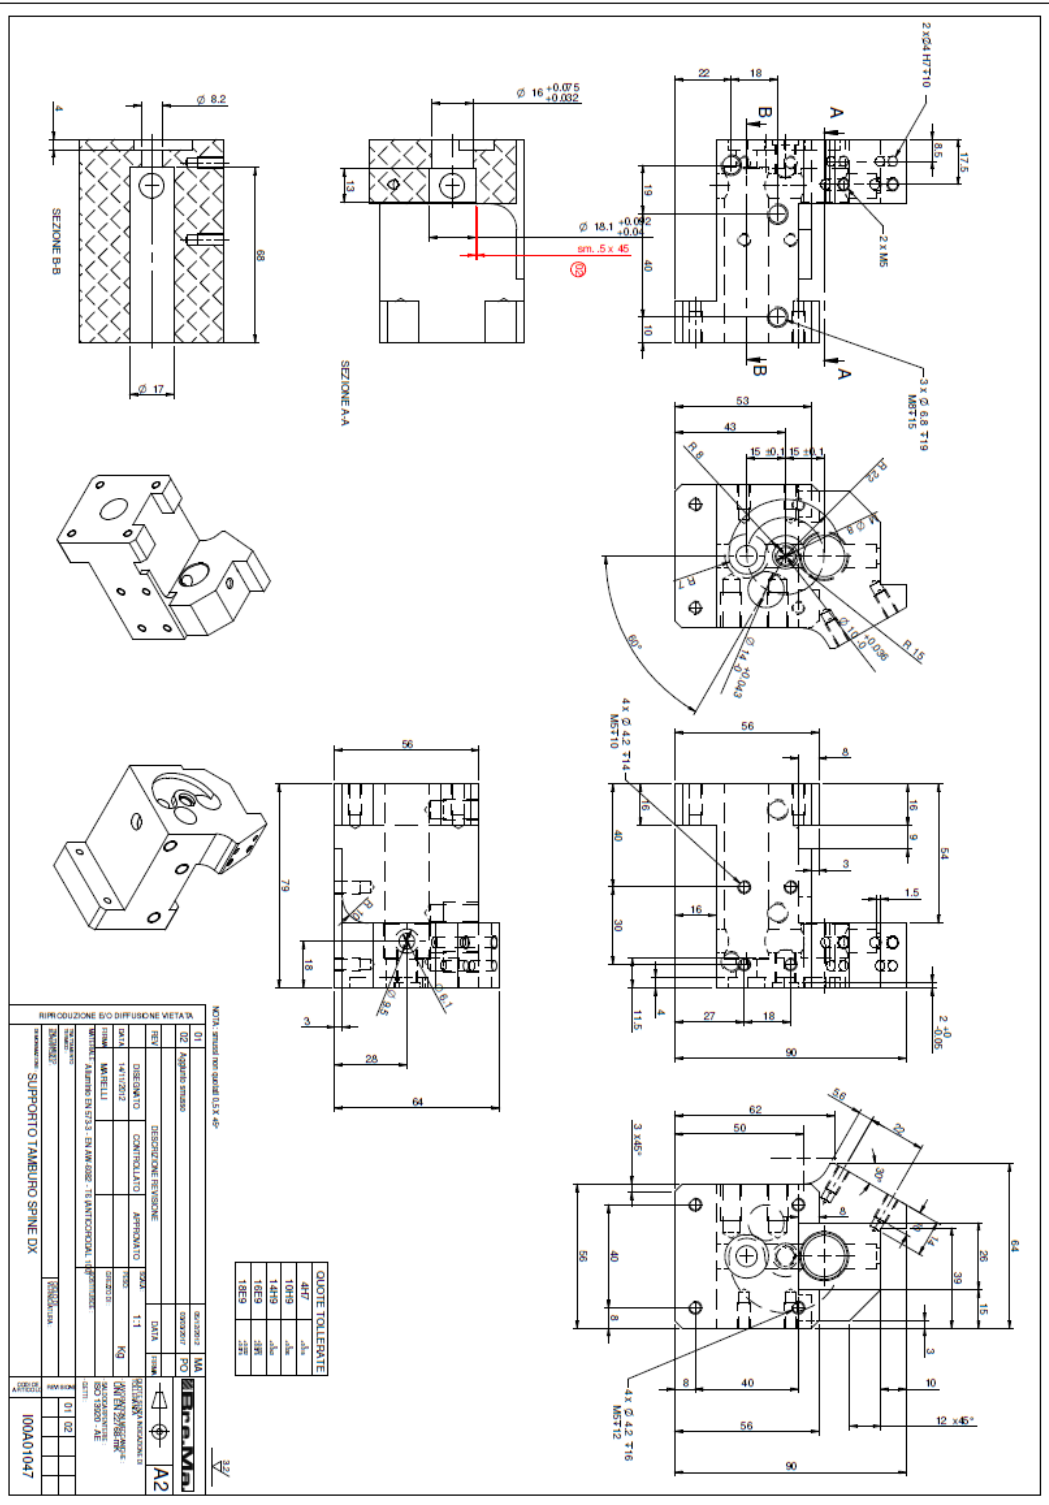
Disegno tecnico SUPPORTO TAMBURO SPINE DX
